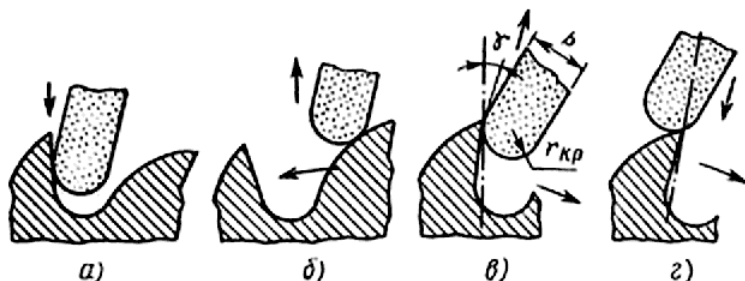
Схема заточки зубьев дисковой пилы по передней и задней поверхностям
